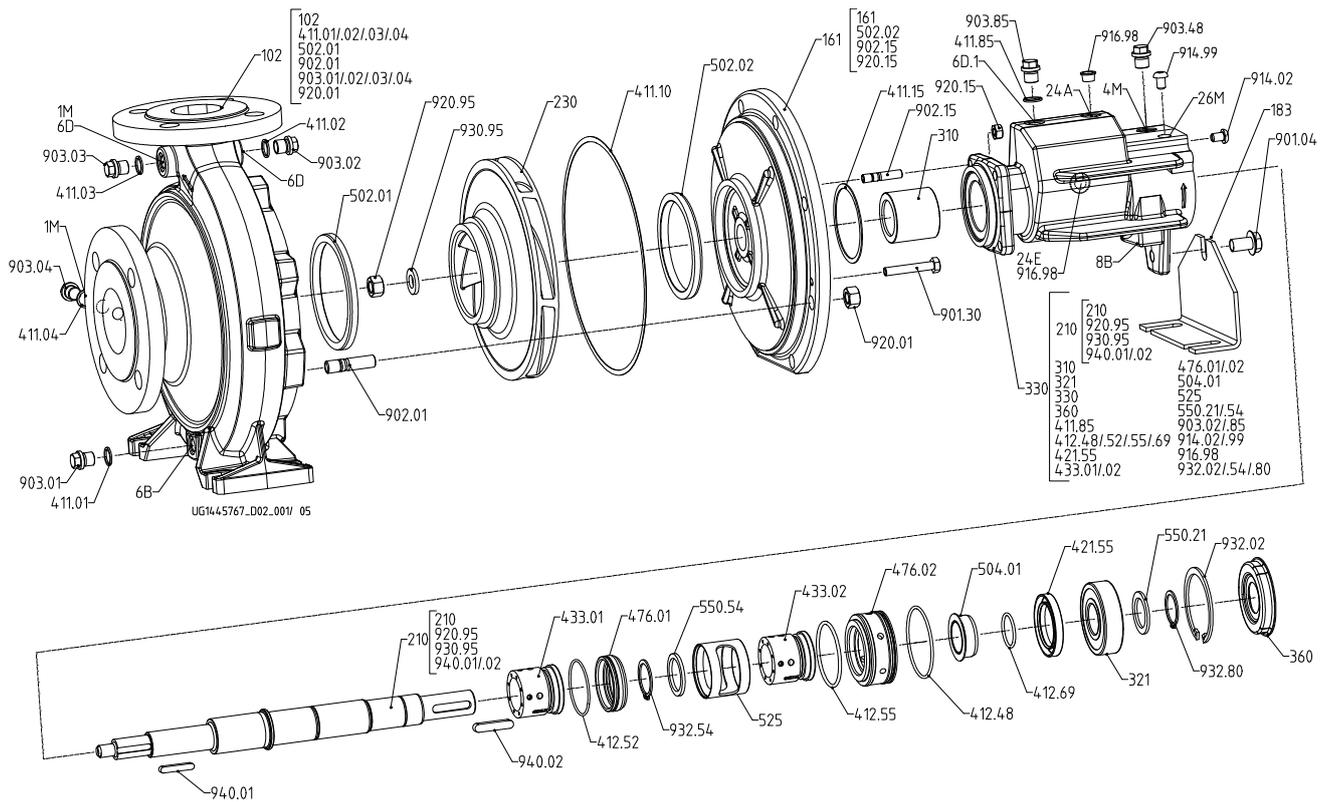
Vista detallada de Etanorm SYT, soporte de cojinetes WS_25_LS con cierre mecánico doble
